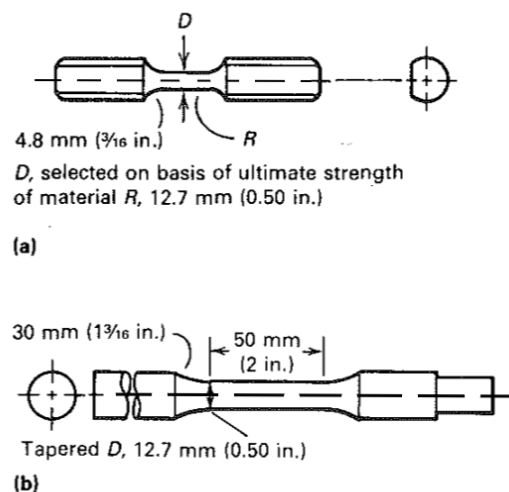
Éprouvettes d'essai de fatigue typiques -1-
